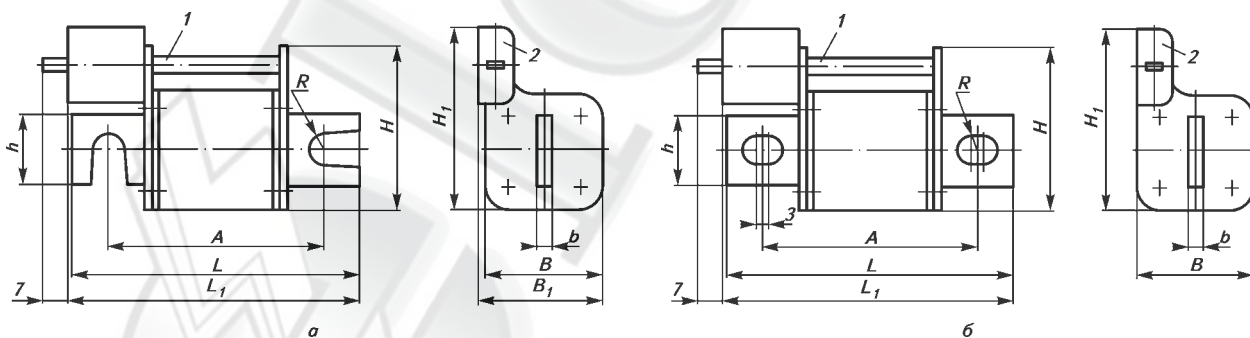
Общий вид, габаритные, установочные присоединительные размеры и масса предохранителей:
